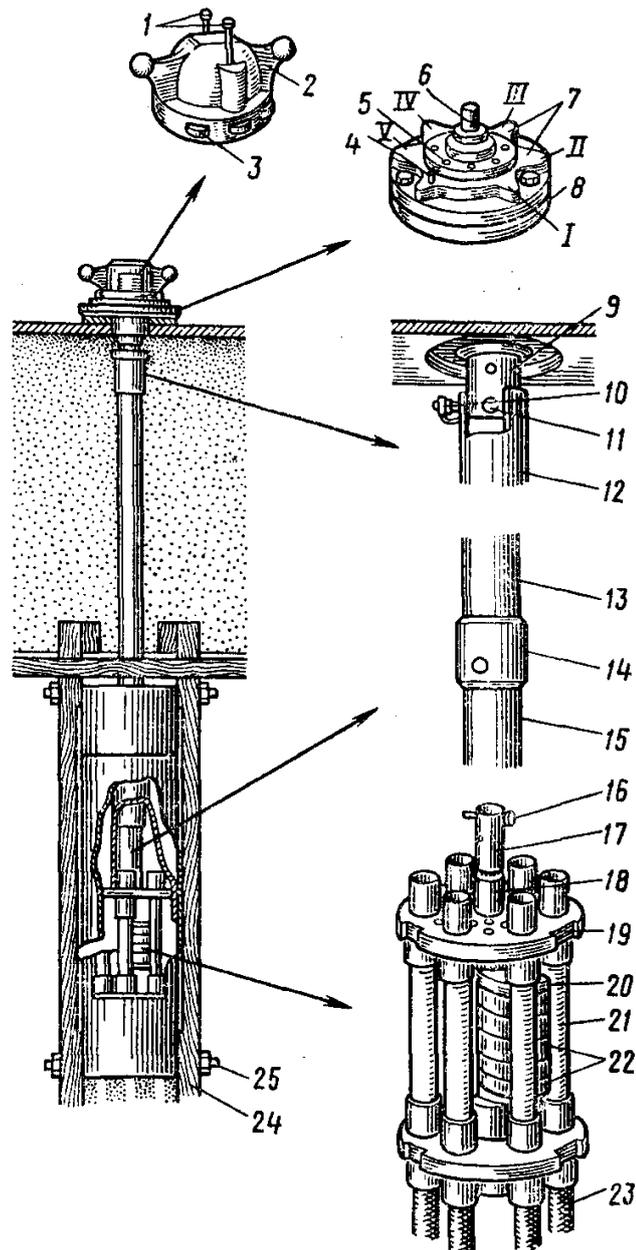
Общий вид и детали однофазного переключателя барабанного типа: 1 - стопорные болты; 2 - колпак привода; 3 - указатель положения; 4 - упор; 5 - отверстие для стопорного болта; 6 - вал привода; 7 - выступы на крышке сальника; 8 - фланец; 9 - втулка привода; 10, 16 - штифты; 13 - штанга; 15 - валик нижней муфты; 17 - втулка переключателя; 18 - изоляционная втулка вала переключателя; 19 - гетинаксовый диск; 20 - коленчатый вал; 21 - контактный стержень; 22 - контактные кольца; 23 - кабель; 24 - вертикальная деревянная планка; 25 - шпилька из изоляционного материала; 1—V - указатели положения переключателя; 11 - валик; 12 и 14 - верхняя и нижняя муфты
